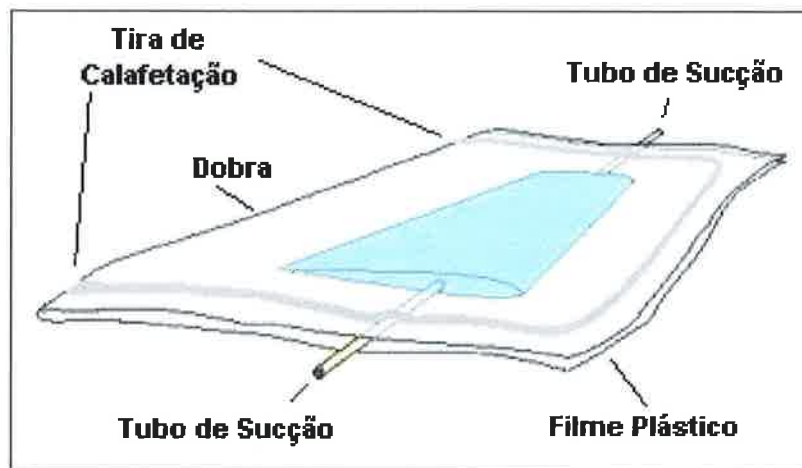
Invólucro do processo *vacuum bagging*. (Adaptado de Fouquet, 1996).
